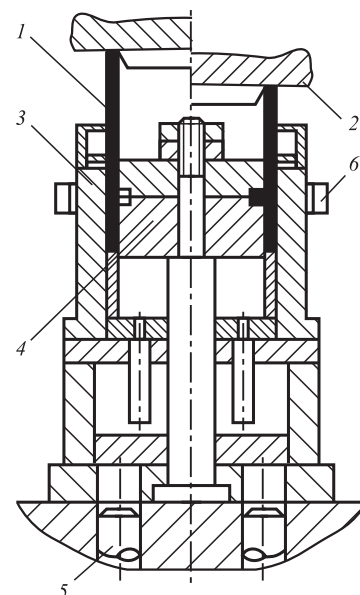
Штамп для выдавливания утолщения на трубе: 1 — заготовка; 2 — нажимной пуансон; 3 — корпус; 4 — матрица; 5 — выталкиватель; 6 — индуктор ТВЧ
